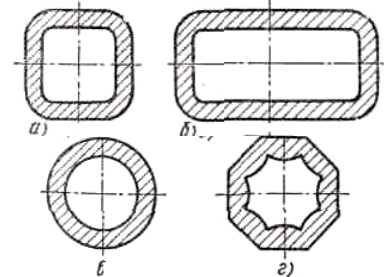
Поперечні перетини виливниць для розливання сталі в злитки.
